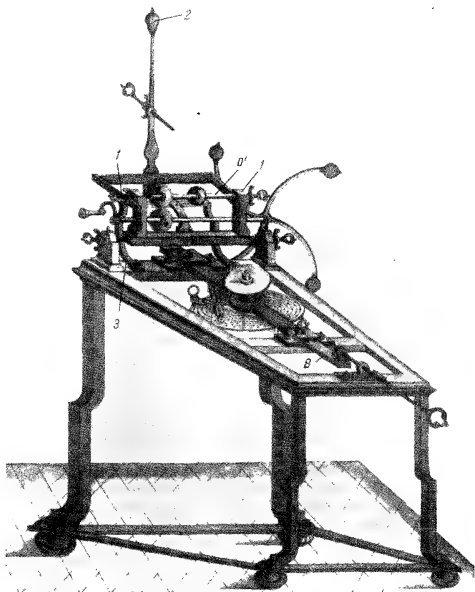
Зуборезно-фрезерный станок, изготовленный А. К. Нартовым. Около 1724 г. Рукопись «Театрум Махинарум» А. К. Нартова.
